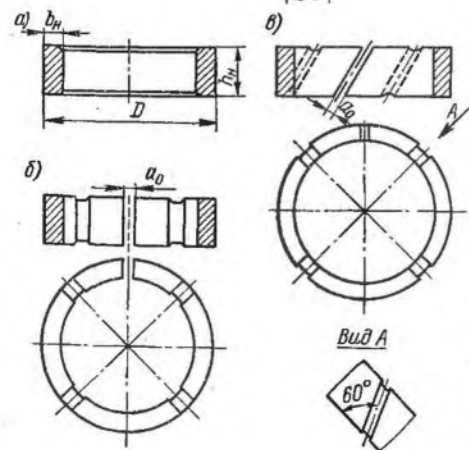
Конструкция опорно-направляющих колец: а — цельная; б — разрезная с разгрузочными канавками прямыми по внутренней поверхности; в — разрезная с разгрузочными канавками, наклонными на наружной поверхности
